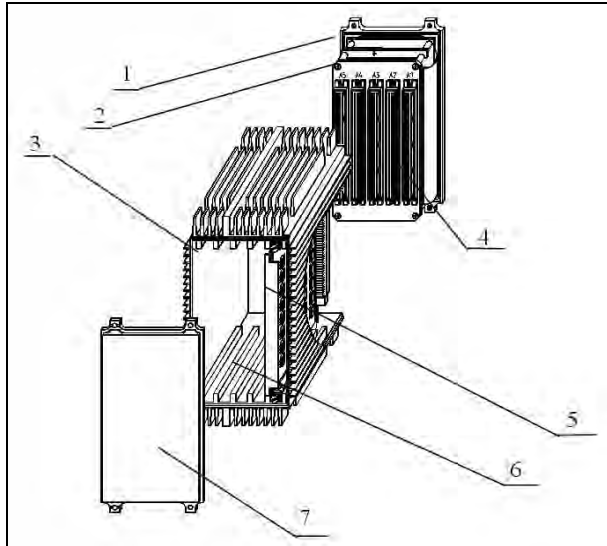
Уніфікована конструкція електронного блока: 1 – задня панель; 2 – об'єднуюча плата; 3 – корпус; 4 – гнучка плата; 5 – комірка; 6 – клин; 7 – передня панель
